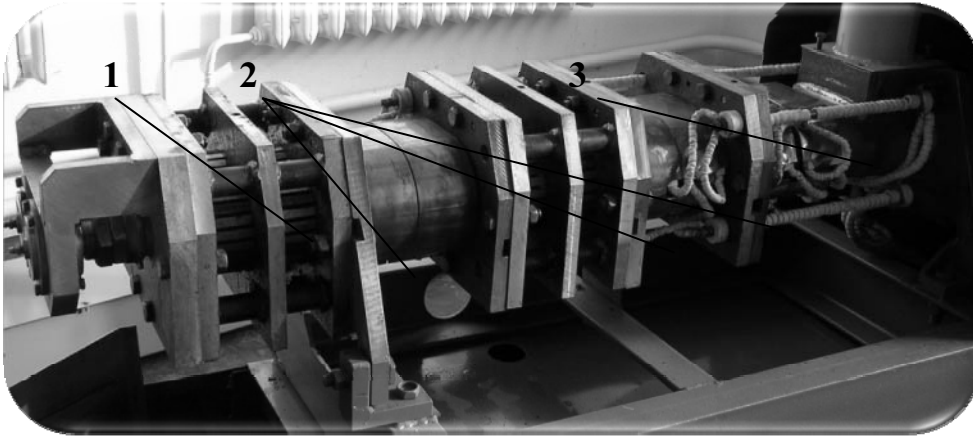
Зовнішній вигляд корпуса екструдера ЕК 75/1200:
